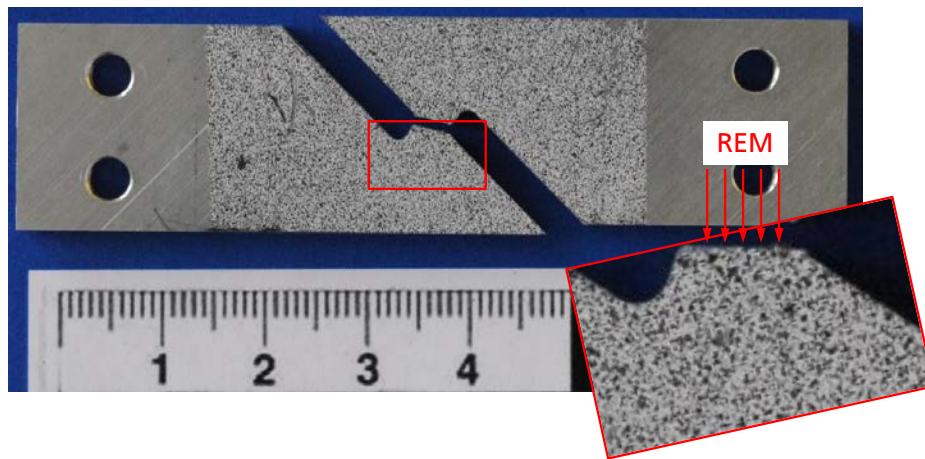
Oberflächenansicht einer gebrochenen Scherzugprobe mit Kennzeichnung der im REM untersuchten Bruchfläche
